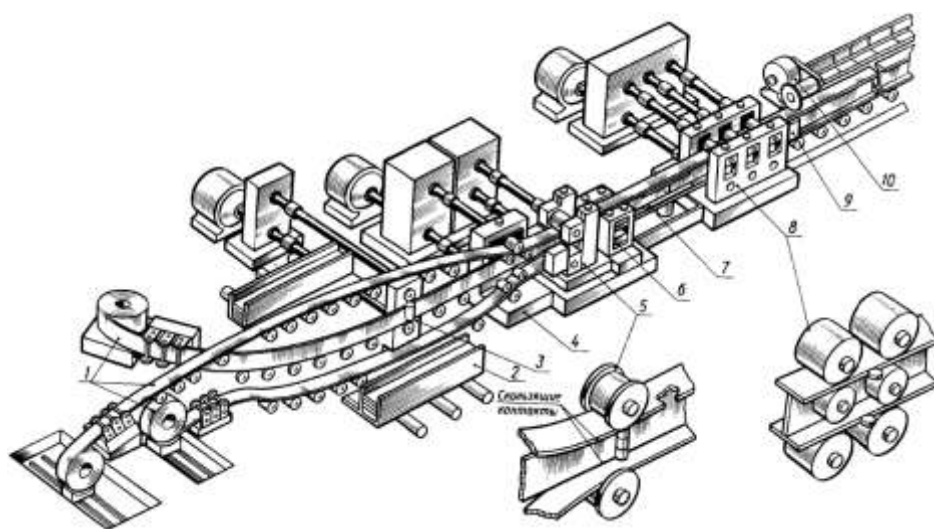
Схема агрегата для изготовления двутавровых профилей сваркой ТВЧ
